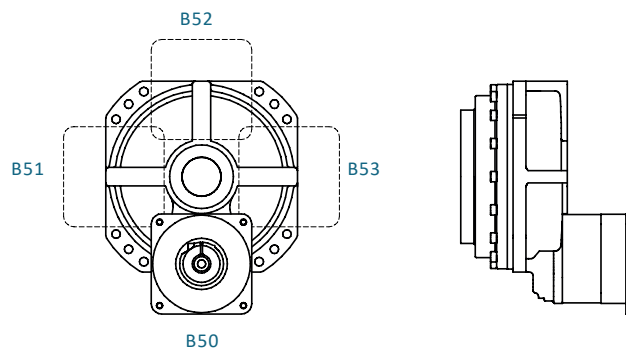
Einbaulagen – Antrieb horizontal, Eingangsposition wahlweise
